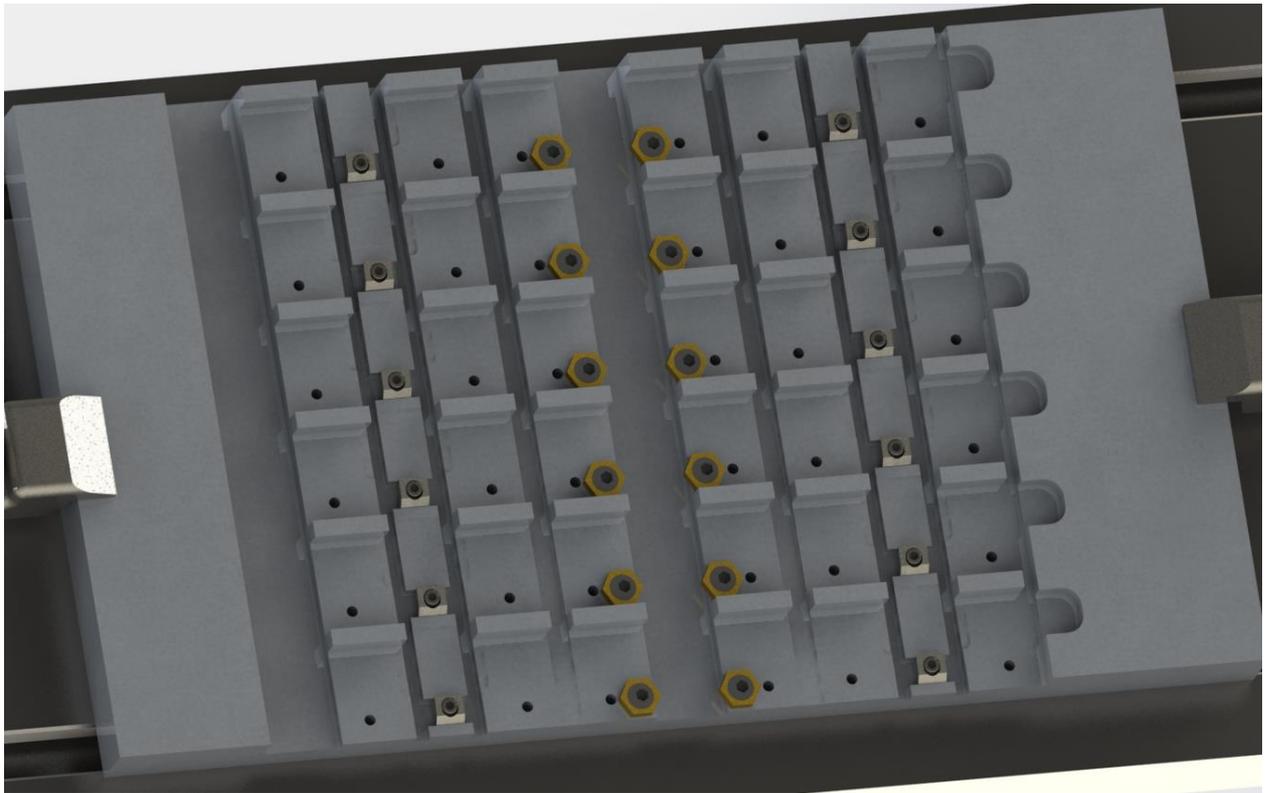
Utillaje 04, disposición para las tres primeras operaciones.
